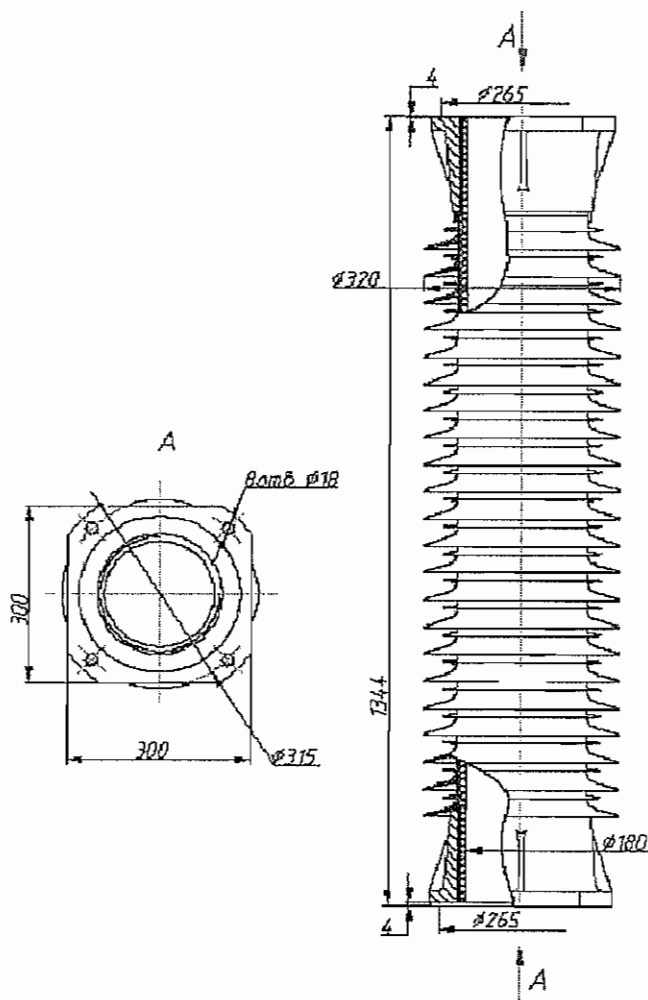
Габаритный чертеж покрышки ППТЭ-110-4 УХЛ1
